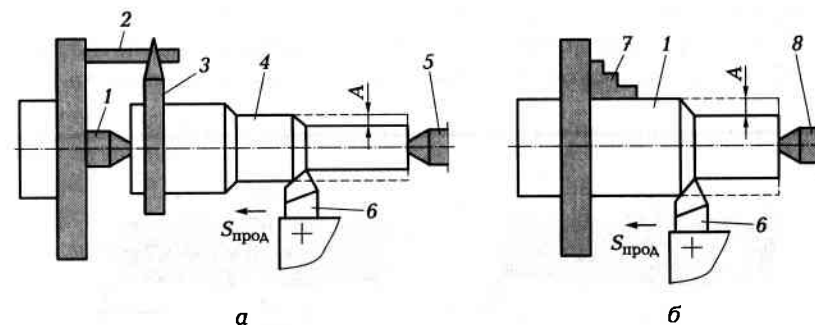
Схемы установки заготовки на токарном станке: а — в центрах; б — в самоцентрирующем патроне
